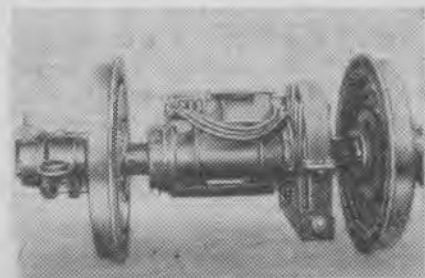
Асинхронный тяговый двигатель с цилиндрическими роликовыми моторно-осевыми подшипниками на оси колесной пары
